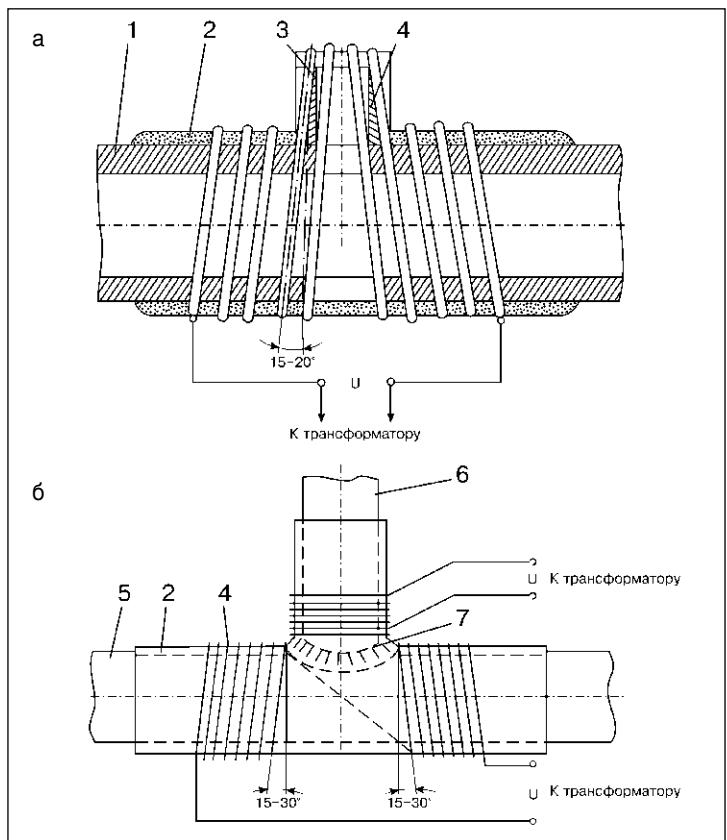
Схемы установки индукторов при местной термообработке сварных соединений штуцеров: а — приварка штуцера к трубе; б — сварной тройник (1 — труба; 2 — теплоизоляция; 3 — индуктор с различным шагом витков; 4 — штуцер; 5 — основание тройника; 6 — патрубок тройника; 7 — сварной шов)
